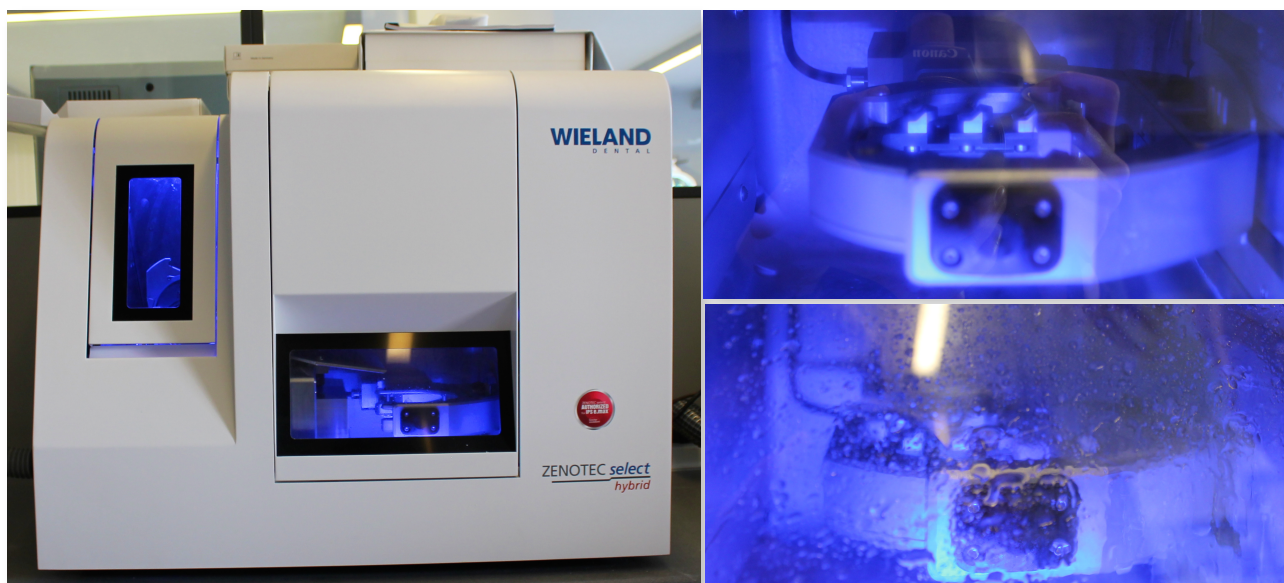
Fresadora Wieland Zenotec (izquierda)
